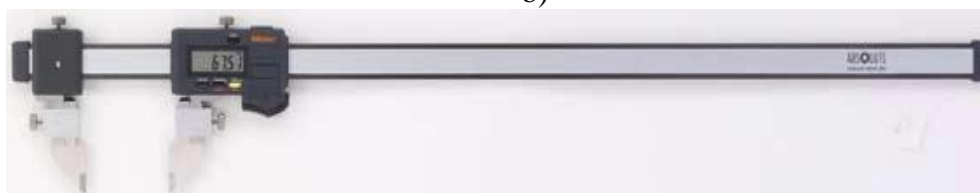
Общий вид штангенциркуля серии 551 с закругленными и удлиненными губками
